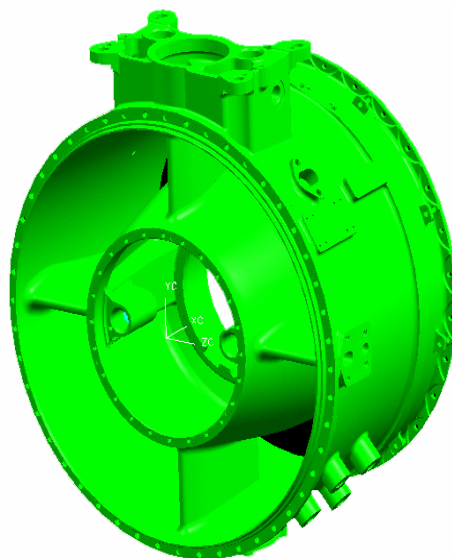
Корпус первой опоры двигателя BK1500- BM
